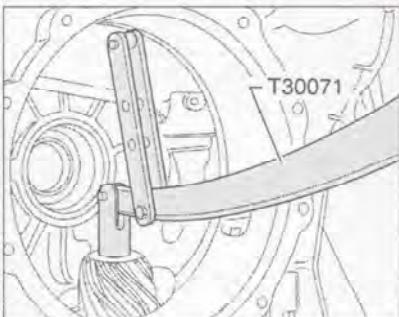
Приспособлением T30071 отожмите вторичный вал так, чтобы наружная обойма малого роликоподшипника прилегала к корпусу коробки передач.
